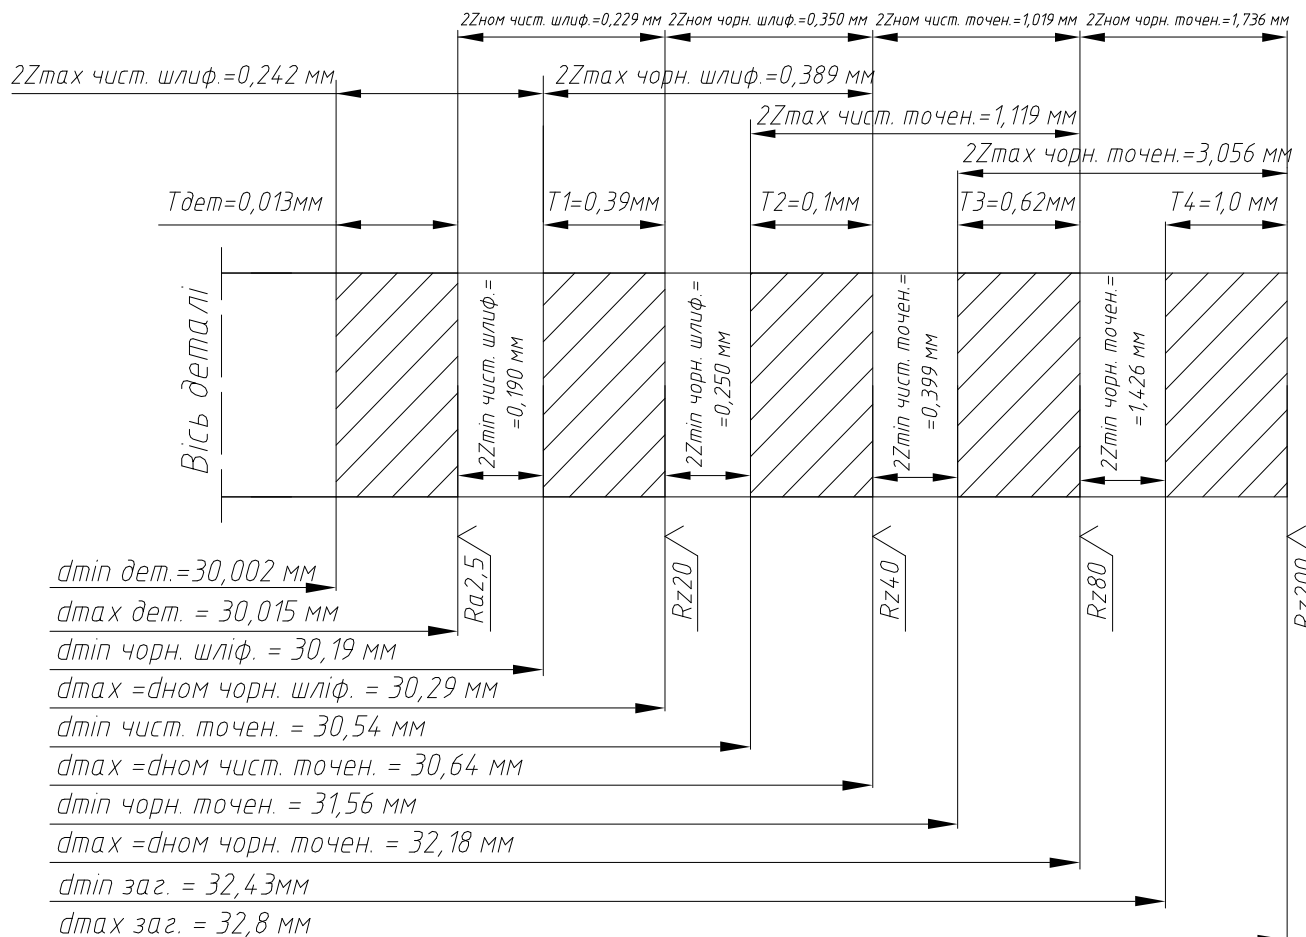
Схема розрахунку припусків для обробки зовнішньої циліндричної поверхні.
